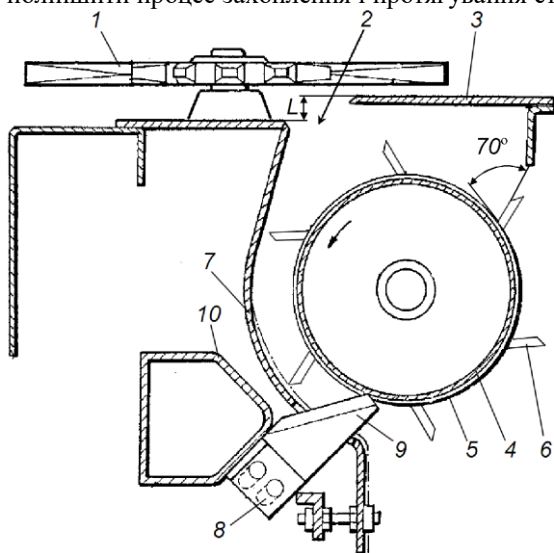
Схема адаптованого качановідокремлювального апарата: 1 – подавальний ланцюг з лапками; 2 – протягувальний простір; 3 – стріперні пластини; 4 – протягувальний валець, 5 – насадка; 6 – загострені протягувальні ребра; 7 – кожух; 8 – регулювальні пази; 9 – система ножів; 10 – рама
